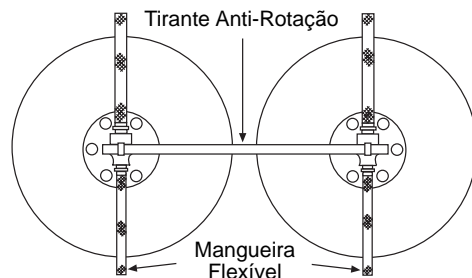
Instalação horizontal do tirante nas orelhas da cabeça.
